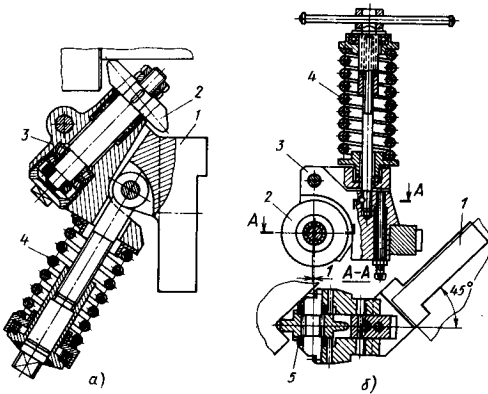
Однорولیковые приспособления для обкатывания переходных поверхностей: а — наклонным роликом; б — клиновым роликом
